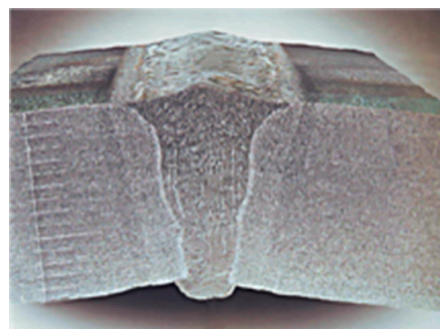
Сварка в один проход металла толщиной 15 мм
